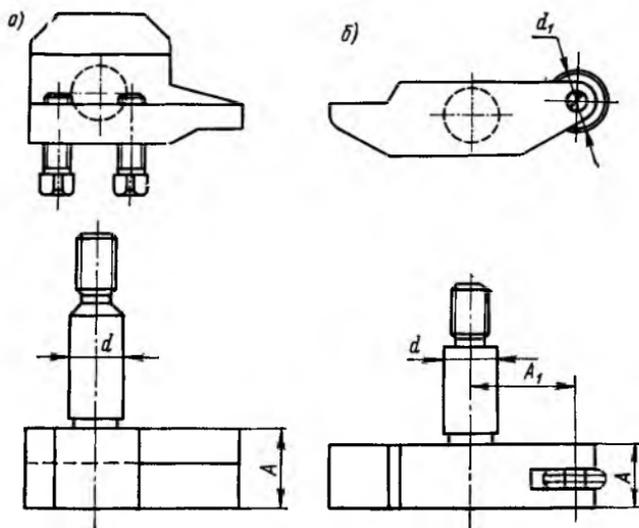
Державки: а — для реза к державкам на передней и задней суппорты; б — для накатного ролика
